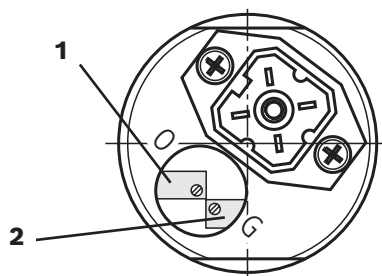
Schwenkwinkelsensor für SYHDFEE
